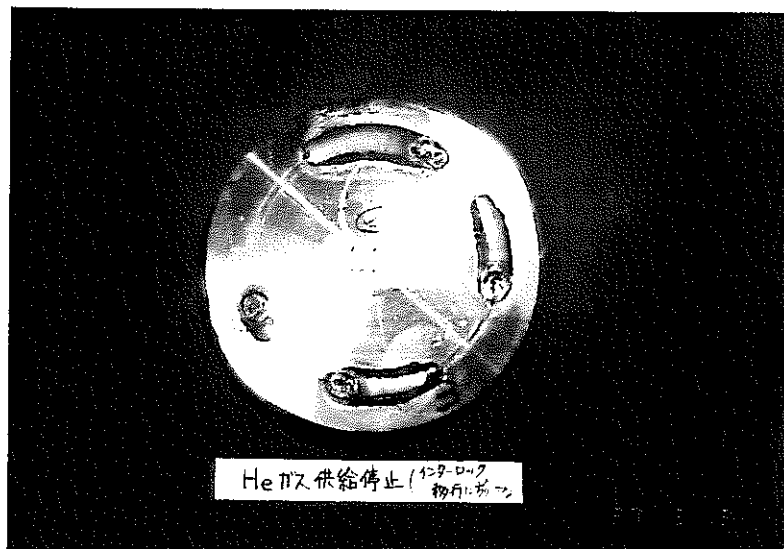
(2/3) 非正常時の溶接停止部外観
